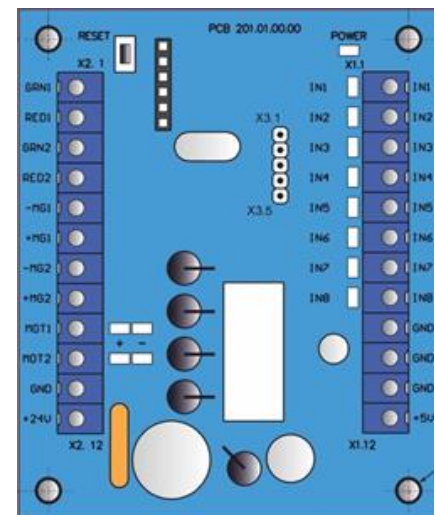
Зовнішній вигляд контролера моторизованого механізму PCB.201.01.00.00
